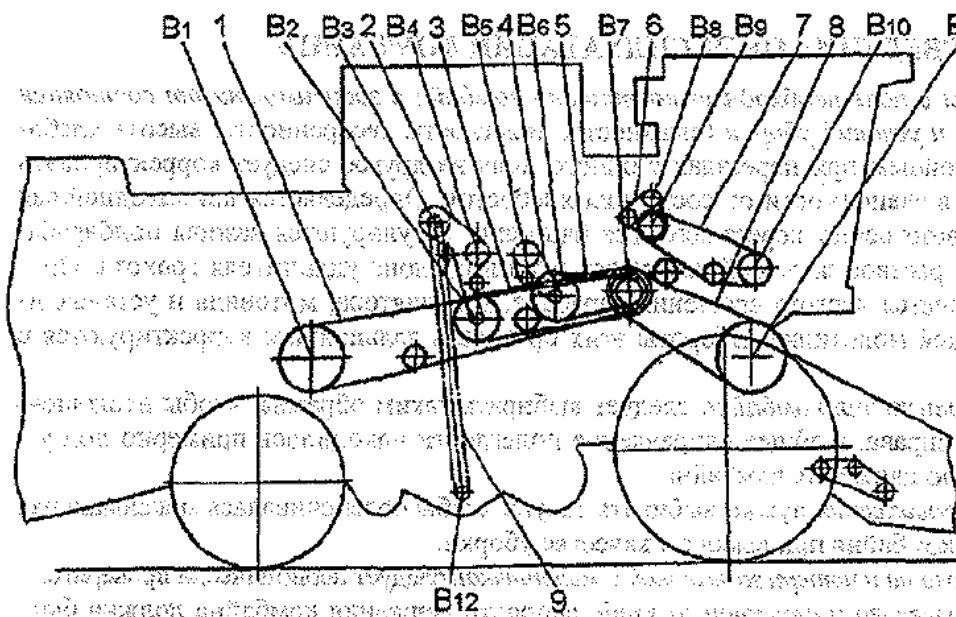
Схема ремённых и цепных передач комбайнов «Дон» (правая сторона): 1- передача на задний контрпривод; 2- верхний вал зернового элеватора; 3- вал горизонтального выгрузного шнека бункера; 4- передача на контрпривод зерновой группы; 5- передача на контрпривод выгрузного устройства бункера;
